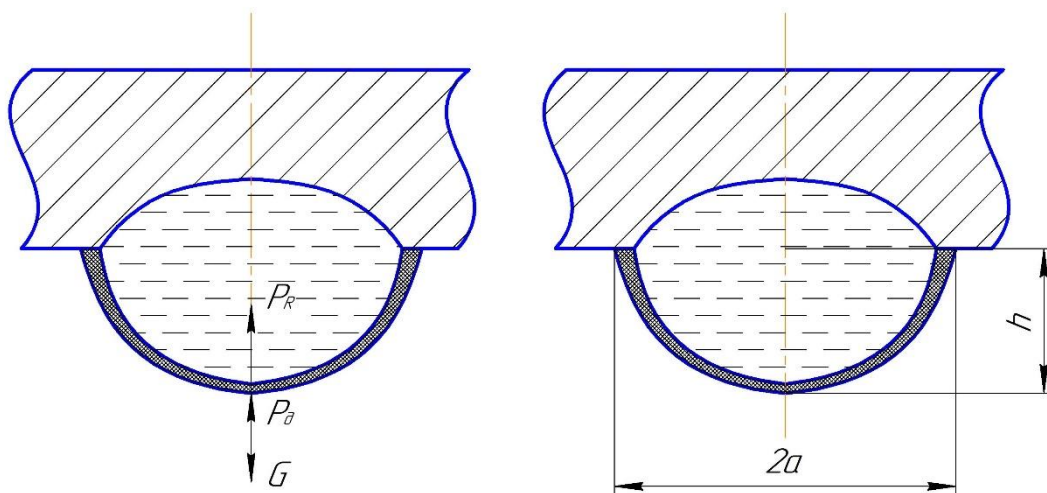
Действие сил на симметричную сварочную ванну при сварке
